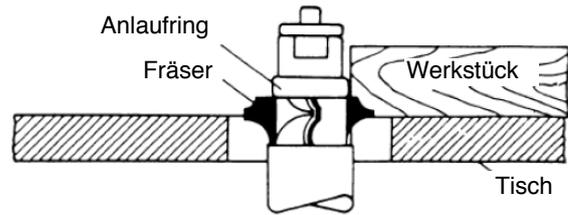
Fräsen mit Anlaufring über dem Fräser
